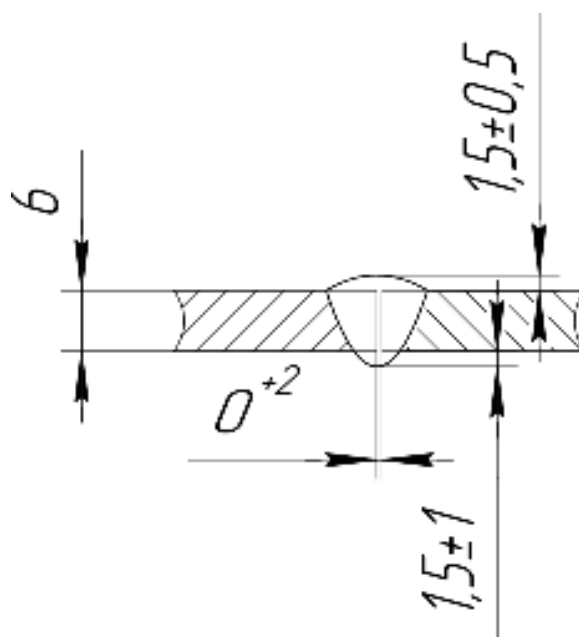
Конструктивные элементы сварного шва С2 ГОСТ14771-76
